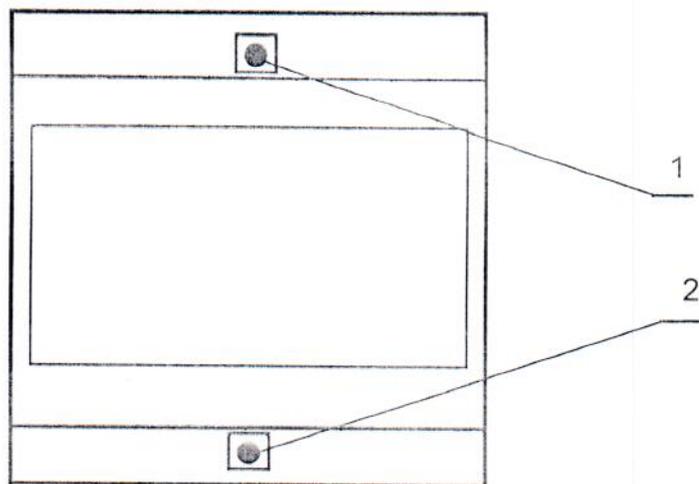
ЭП8554 в корпусе с габаритными размерами 132x81x71 мм
